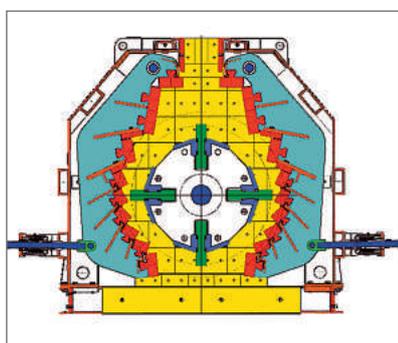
Дробильная камера установки SMR с изнашиваемыми деталями закрытого ротора с четырьмя прямыми ударными билами
